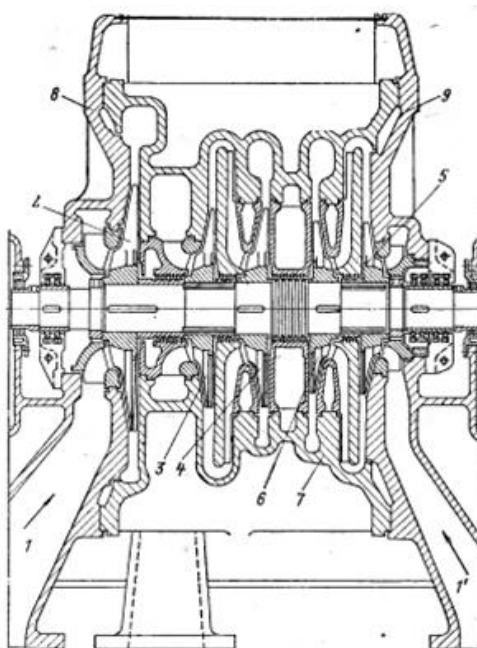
Продольный разрез корпуса турбокомпрессора
